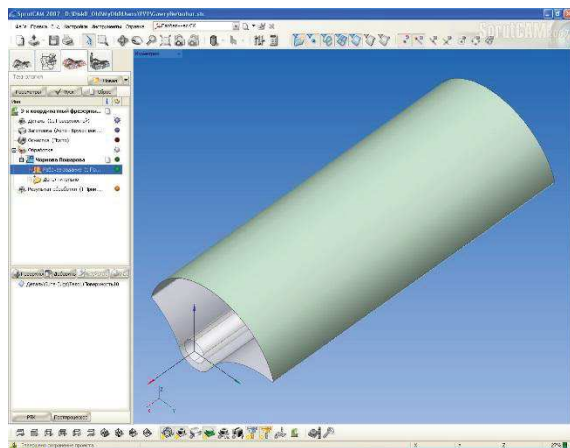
Задання оброблюваної поверхні для операції чорнової обробки
